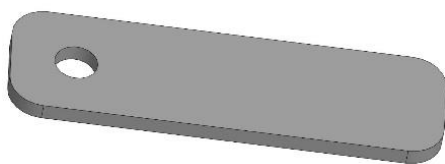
Внешний вид образца для определения скорости коррозии
